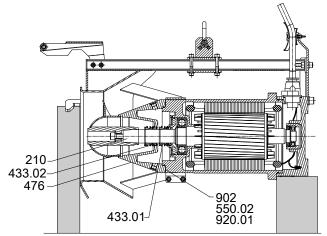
Montaje del cierre mecánico; Amaline 300 con motor 8 6
